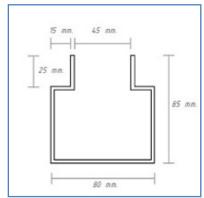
Corte de pata, vista en planta Fuente. Catriel Estanterías
